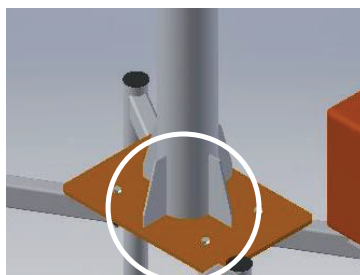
Junta soldada en la unión del plato y la columna.
